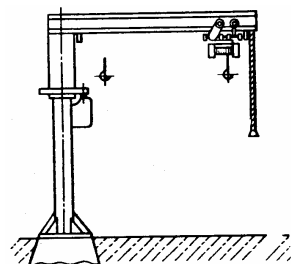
Стреловой стационарный поворотный кран на колонне
